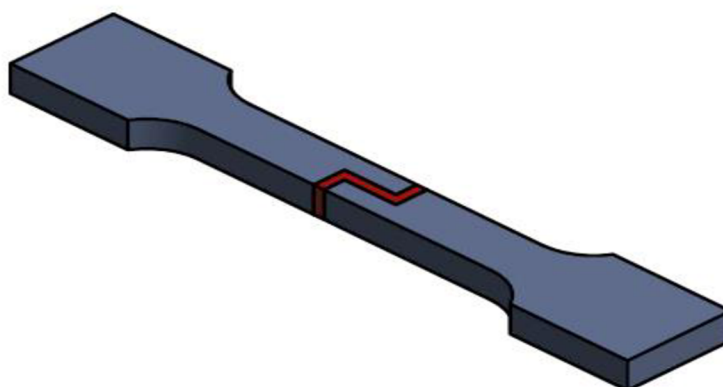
Vzorek pro zkoušku tahem se stupňovitě přeloženým čelem.
